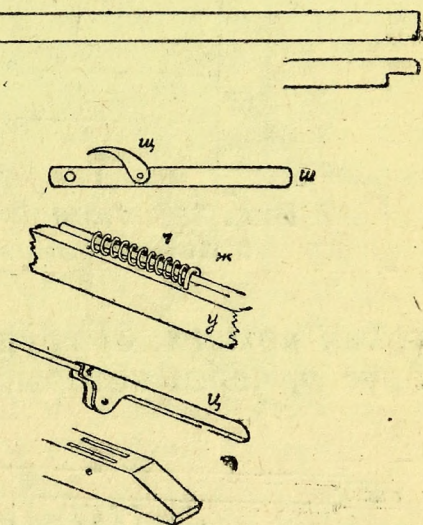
Детали прибора *М*: пружина *ч*, обвивающая железный прут *ф*; дужка *ж* для ее упора в бруске *у*; рычаг *ц* и подним гнезда для укрепления его в бруске *у*.
